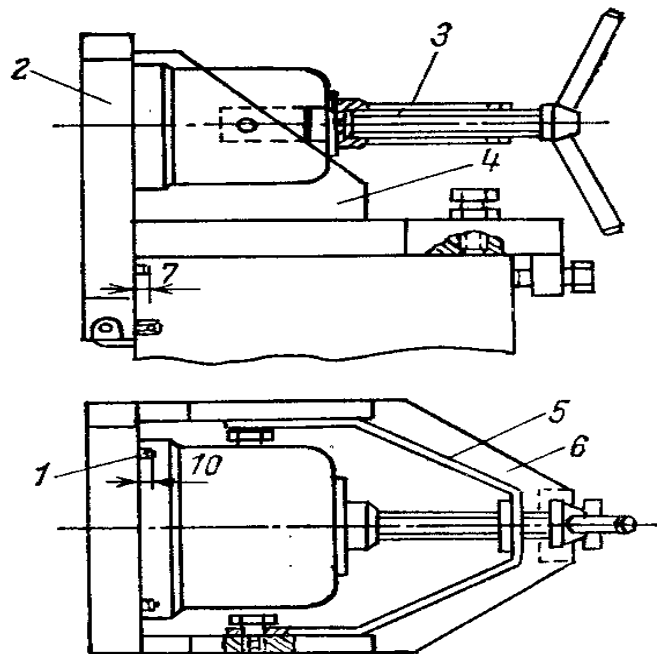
Пристосування для розточування корпусу насоса на токарному верстаті:
